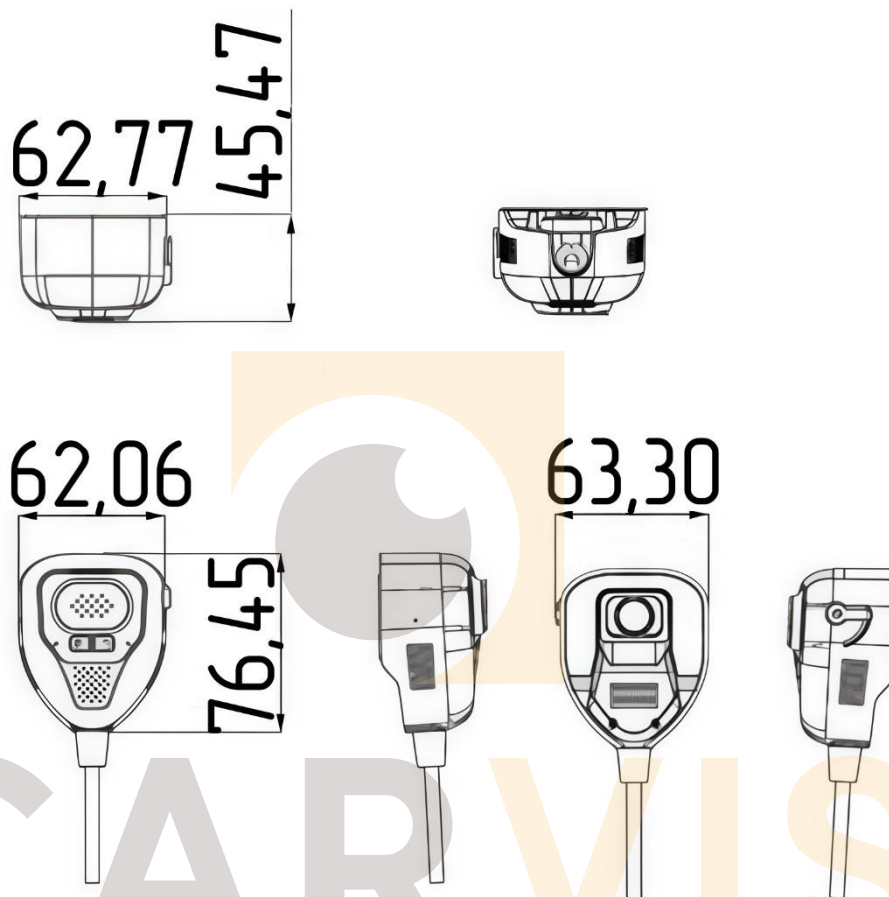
Габаритные размеры и внешний вид камеры CARVIS MC-408 ADAS
